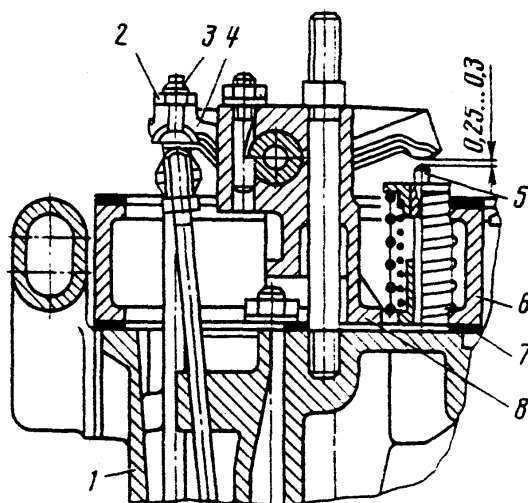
Схема регулювання зазорів у клапанному механізмі.
